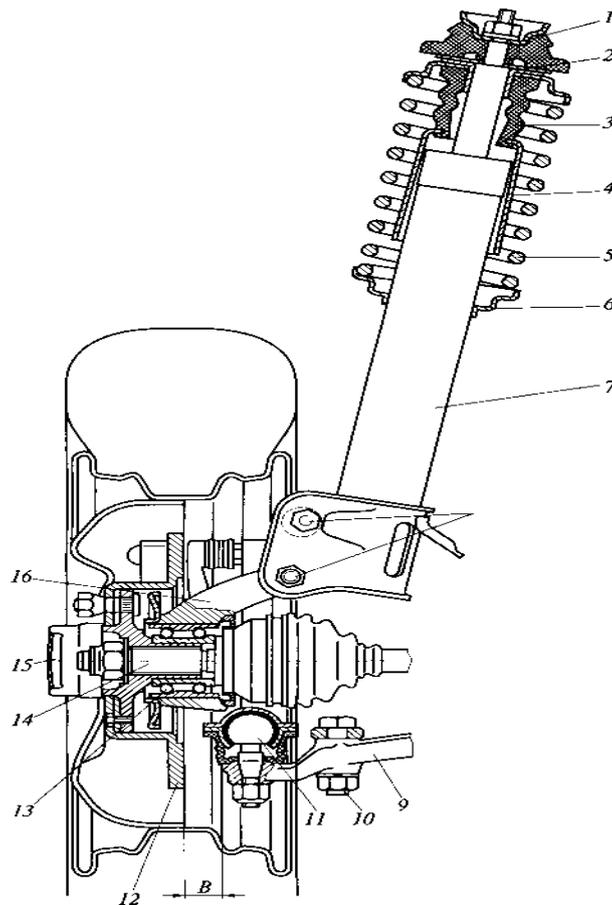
Телескопическая стойка передней подвески в сборе с поворотным кулаком и ступицей колеса: 1 — верхняя опора стойки подвески; 2 — подшипник скольжения; 3 — буфер хода сжатия; 4 — защитный кожух; 5 — пружина подвески; 6 — нижняя опорная чашка пружины; 7 — телескопическая стойка; 8 — болты крепления стойки к поворотному кулаку; 9 — нижний рычаг подвески; 10 — болт крепления растяжки к рычагу подвески; 11 — шаровой шарнир; 12 — диск тормоза; 13 — подшипник ступицы; 14 — шлицевой наконечник корпуса наружного шарнира; 15 — колпак ступицы; 16 — поворотный кулак; В — зона замера зазора в шаровом шарнире подвески.
